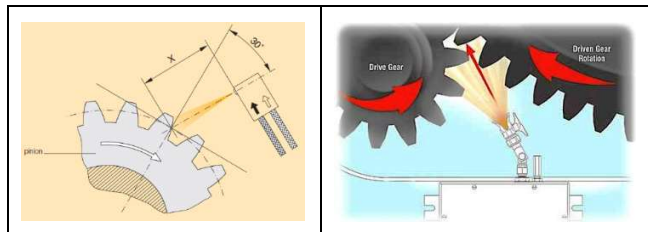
/27 – Padrão de spray de graxa OGL em engrenagem
